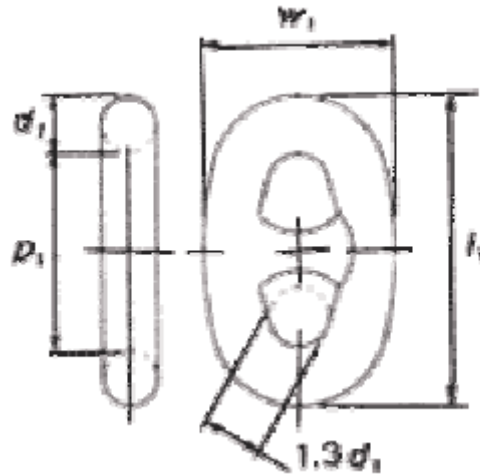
Sección cadena compuesta de acero. Fuente: sistemas de fondeo y anclaje. UPM
